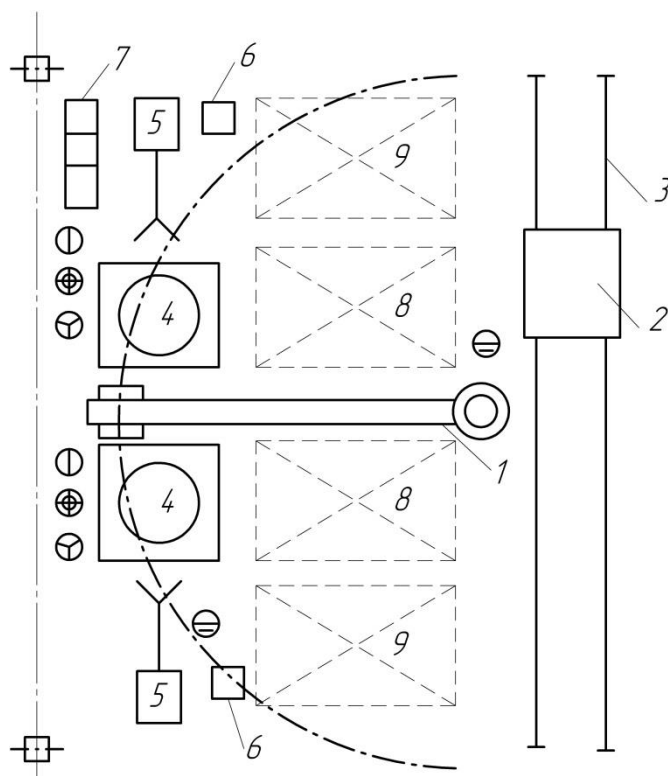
Планировка участка робототехнического комплекса дуговой сварки:
